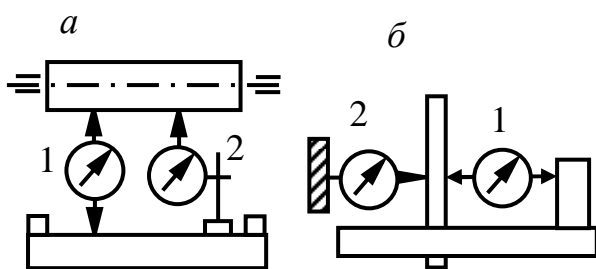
Схемы измерения жесткости станков: *а* – рейсмусового; *б* – фрезерного
